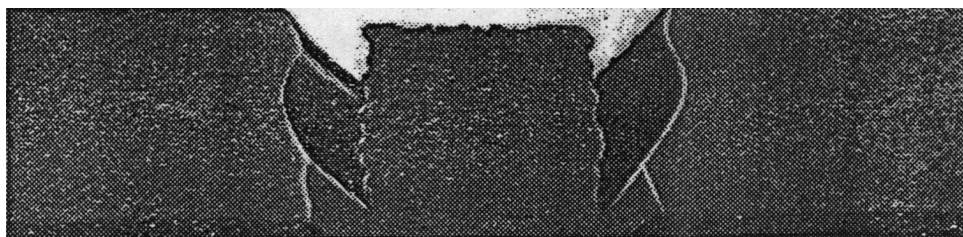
Вигляд зварного зразка, ураженого ножовою корозією
